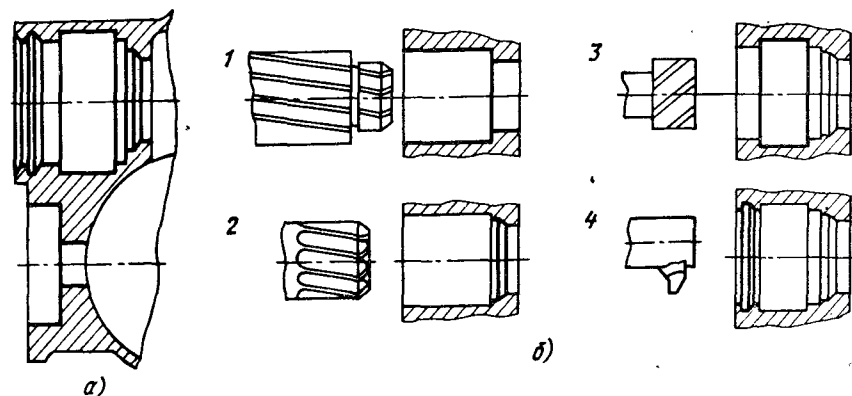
Обработка корпуса на станке с ЧПУ:
